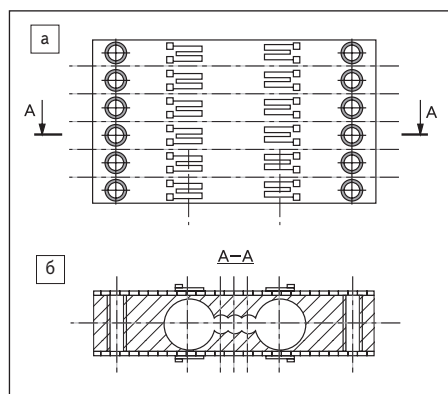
Групповая заготовка для получения 6 упругих элементов:
